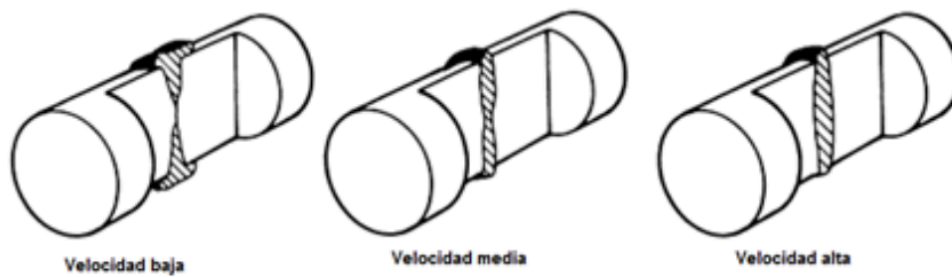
Sección de soldadura por inercia a diferentes velocidades periféricas. [30]
